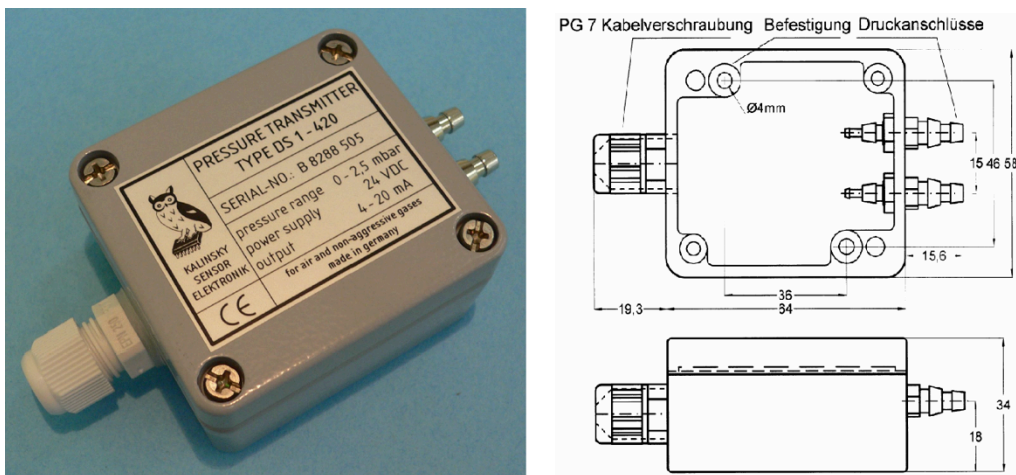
Drucksensor (links), Abmessungen (rechts) [14]
